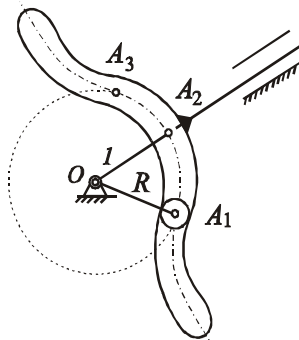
Эквивалентный механизм с поступательно движущейся кулисой
